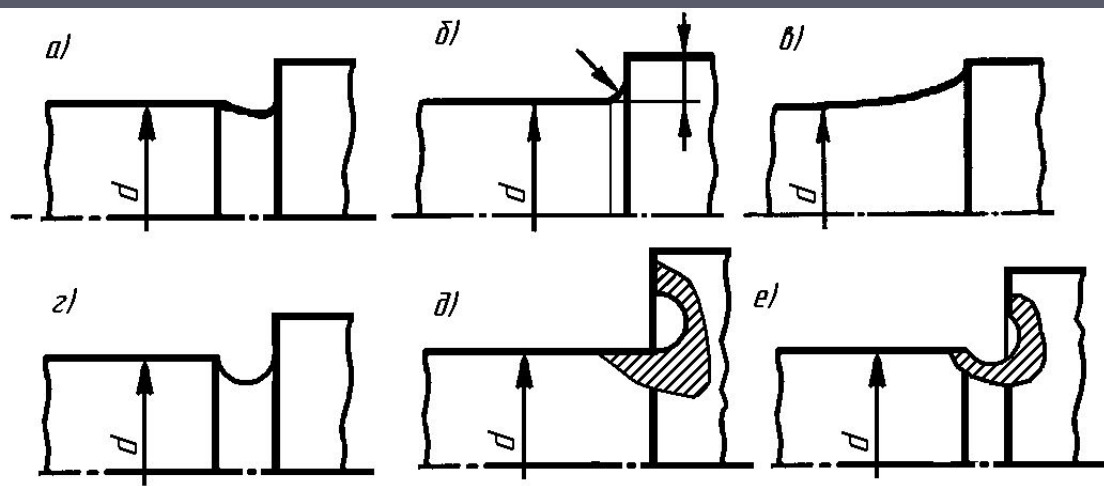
Различные способы оформления переходной части между цилиндрической поверхностью и заплечиком.
